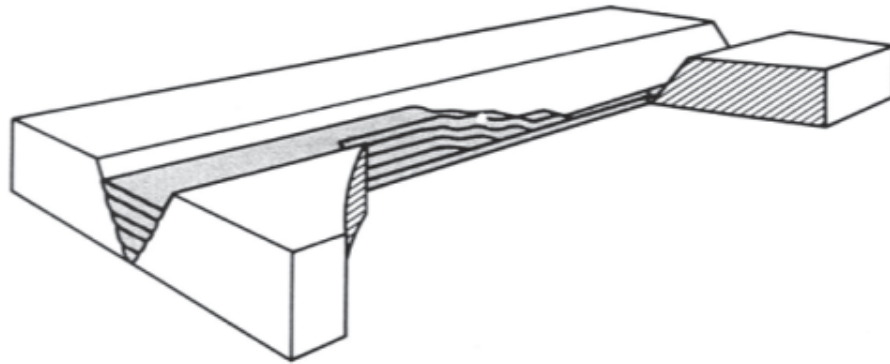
8 Secuencia de soldadura tipo cascada.
